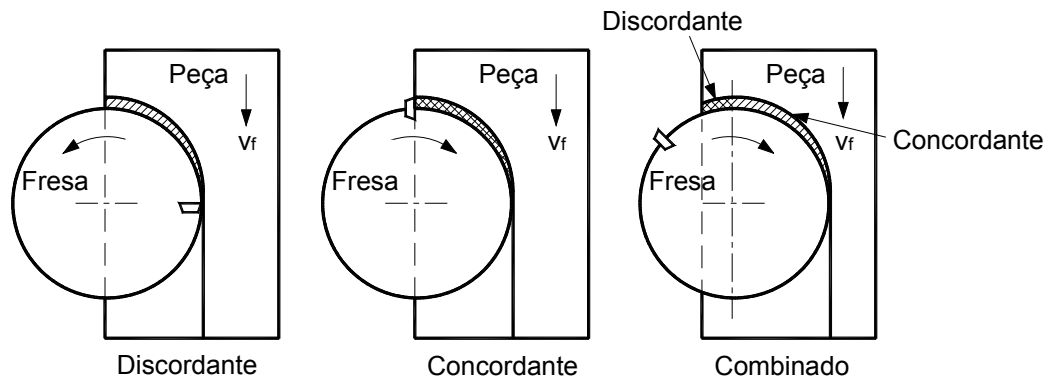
Fresamento discordante, concordante e combinado [22].
